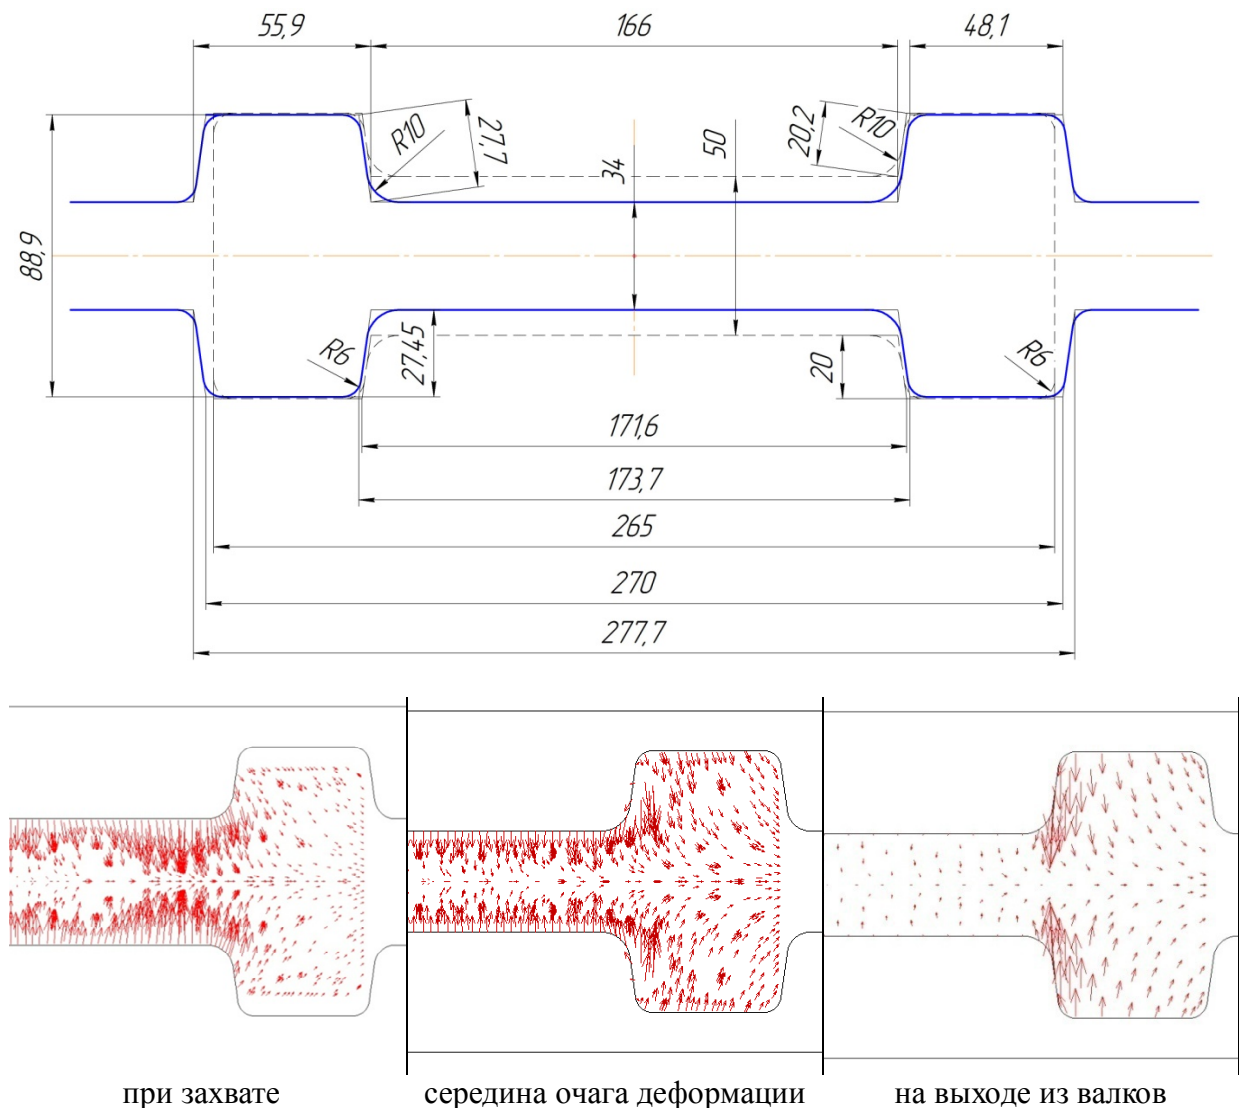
Чертеж калибра и векторные поля скоростей
